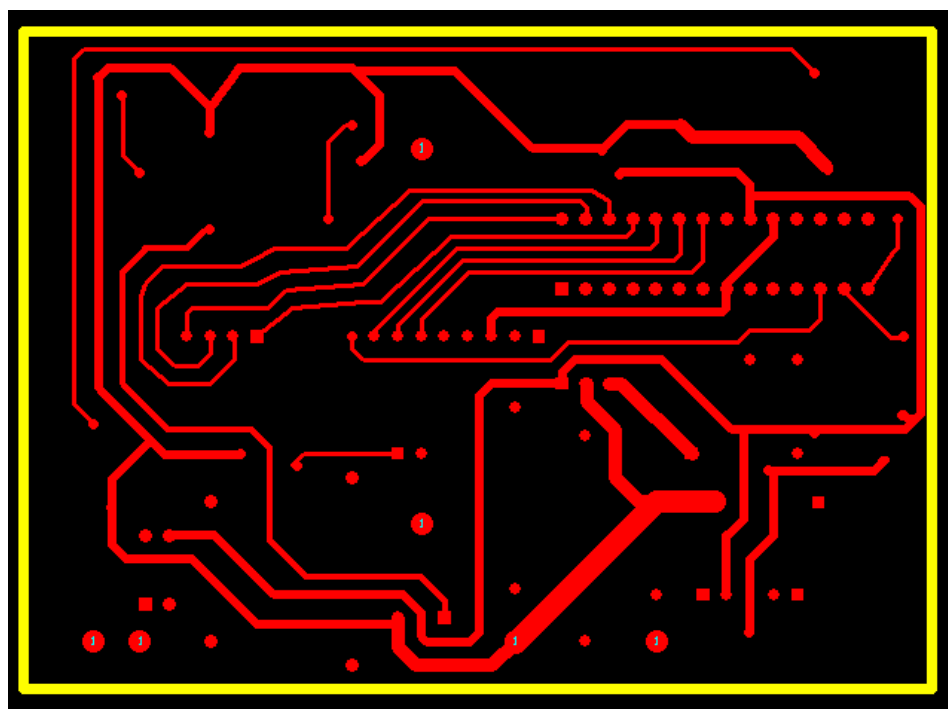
Tarjeta electrónica del dispensador de energía, cara de soldadura.
